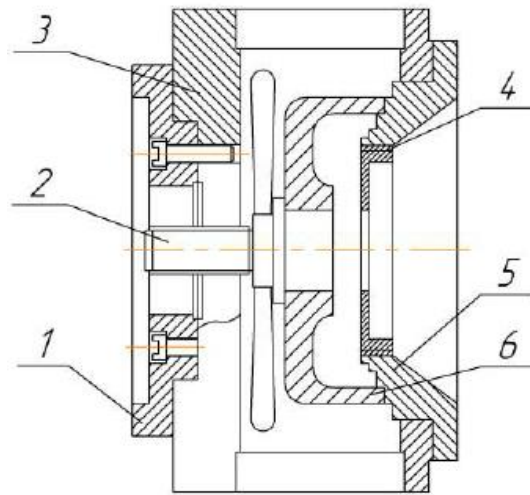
Схема шайби: 1 - оправка; 2 - гвинт; 3 - корпус; 4 - кришка; 5 - щока; 6 - торцевий щит електродвигуна серії 4А.
